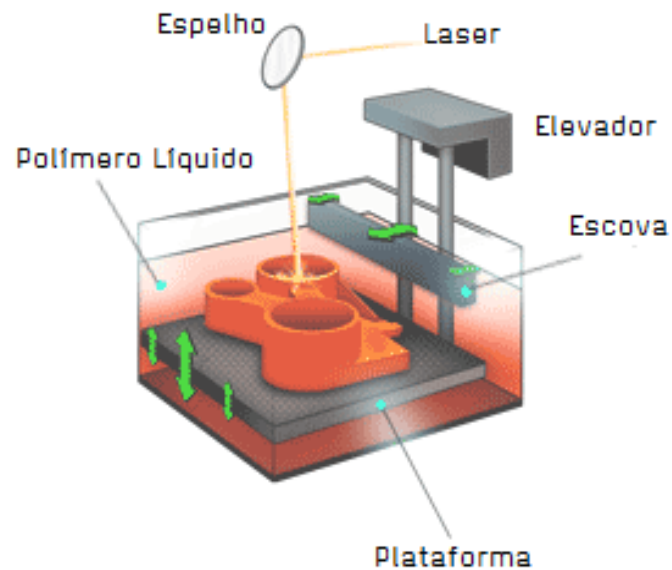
Processo de estereolitografia, SLA [adaptado de <http://www.ccc.gb.com/stereolithography-sla-process-prototyping-techniques-for-injection-moulding-components.php>]
